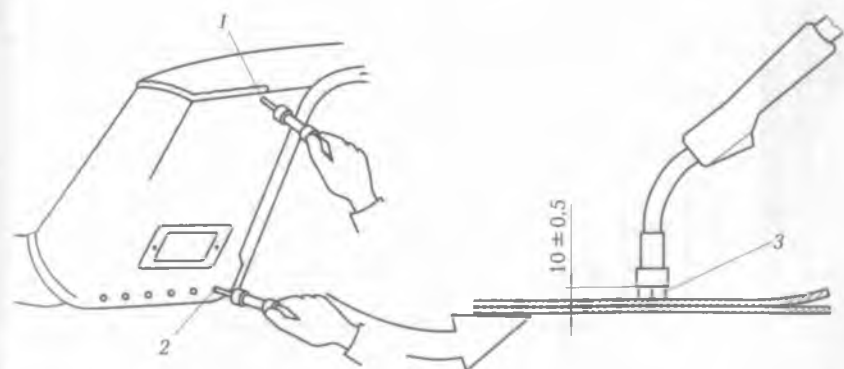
Сварка панели крыши автомобиля:
